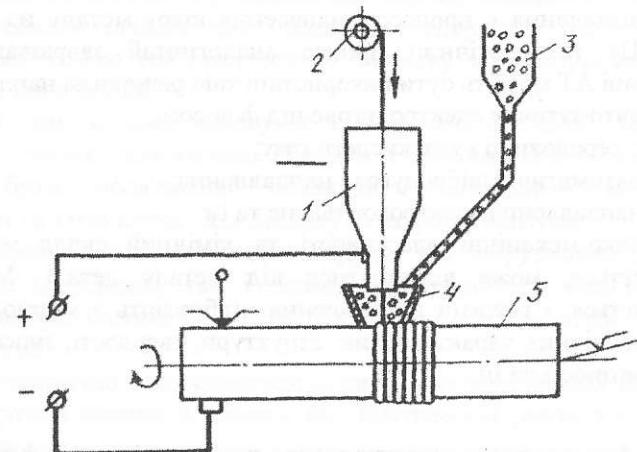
Принципова схема автоматичного електродугового наплавлення деталей під флюсом: 1 – наплавний апарат; 2 – касета з дротом; 3 – бункер з флюсом; 4 – електродний дріт; 5 – деталь, що наплавляється
